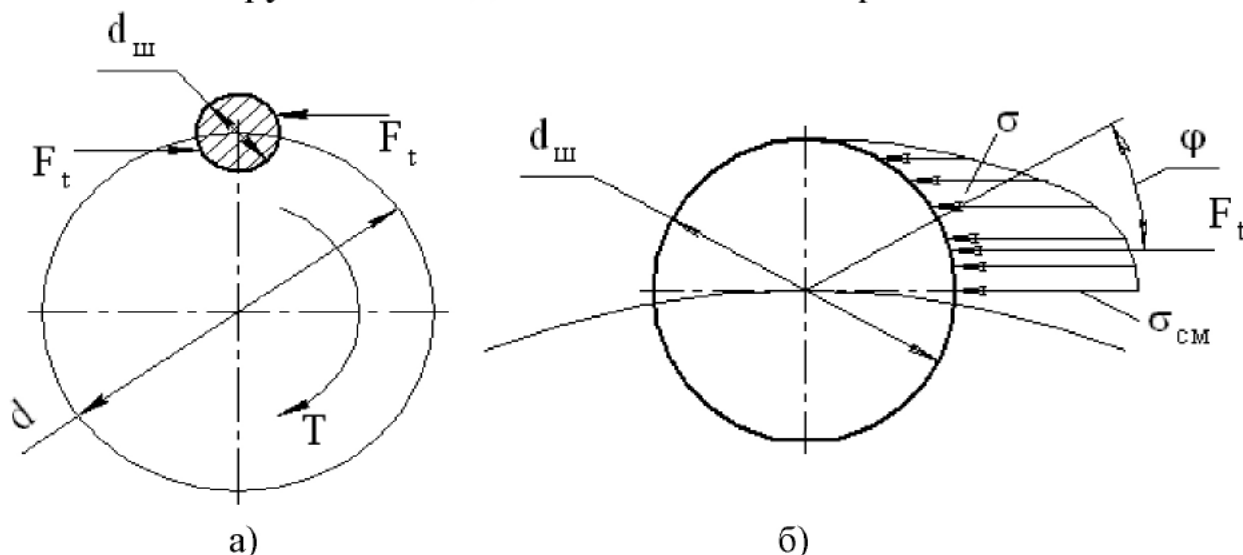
Схема нагружения соединения с круглой шпонкой
